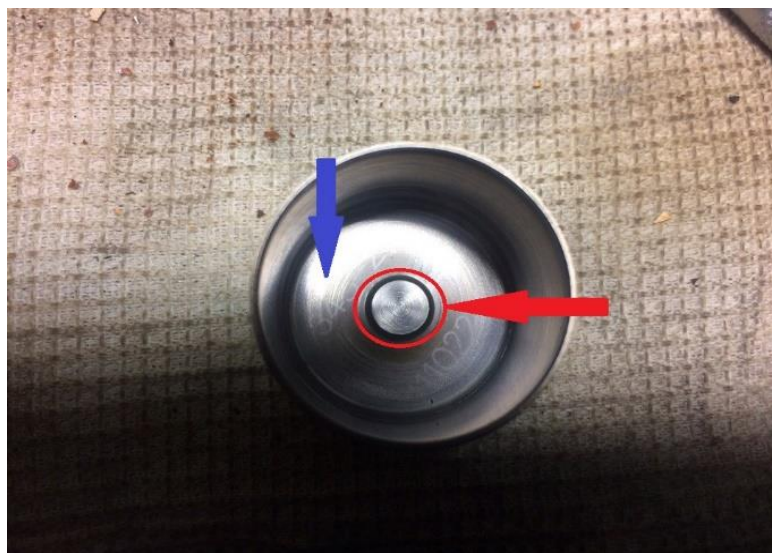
Внутренняя рабочая поверхность толкателя
